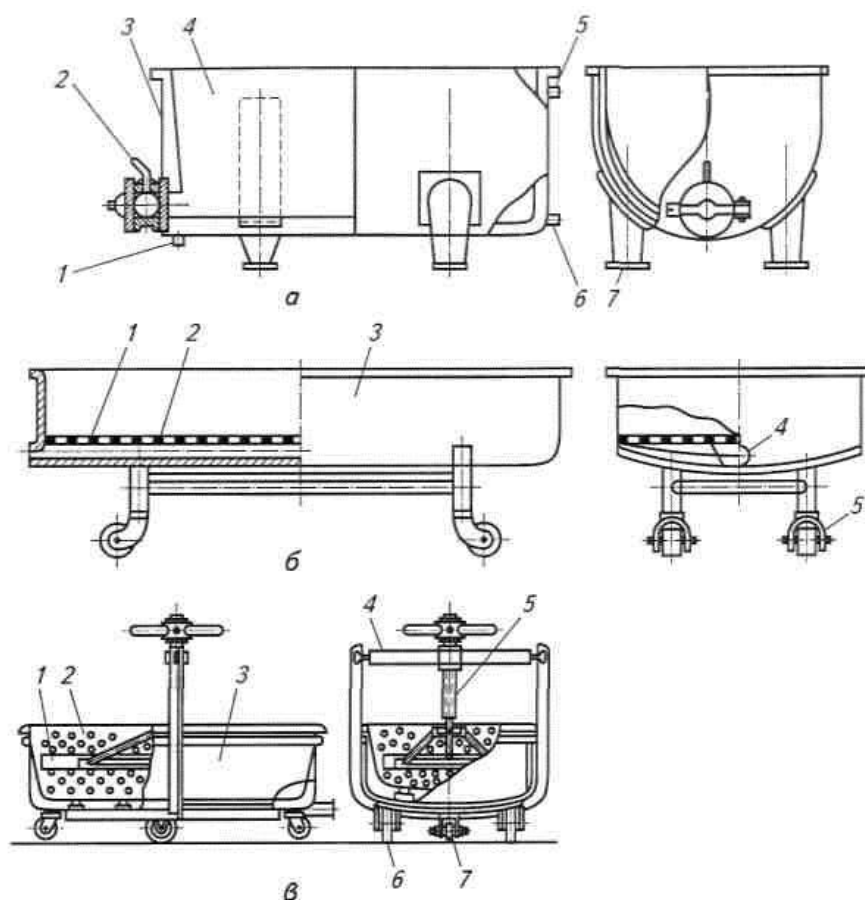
Творожные ванны: а — ванна вместимостью 2,5 м<sup>3</sup>: 1, 5, 6 —сливной, переливной и заливной патрубки; 2—шиберный кран; 3 — рубашка; 4 — ванна; 7—опора; б—ванна самопрессования: 1 — решетка; 2 — тележка; 3 — ванна; 4—сливной патрубок; 5 —колесо; в —пресс-ванна: 1 — нажимная плита-решетка; 2— ванна внутренняя; 3— ванна внешняя; 4— перекладина; 5 —винт; 6, 7—колеса
